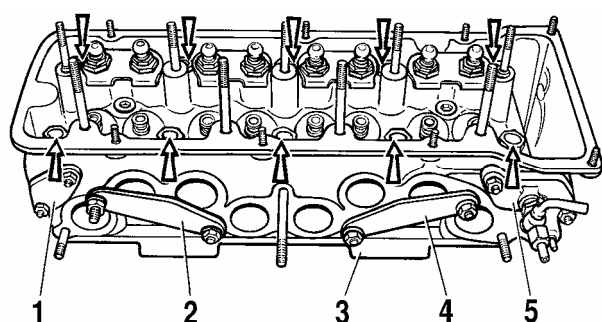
Проверка герметичности головки цилиндров на приспособлении А.60334:
